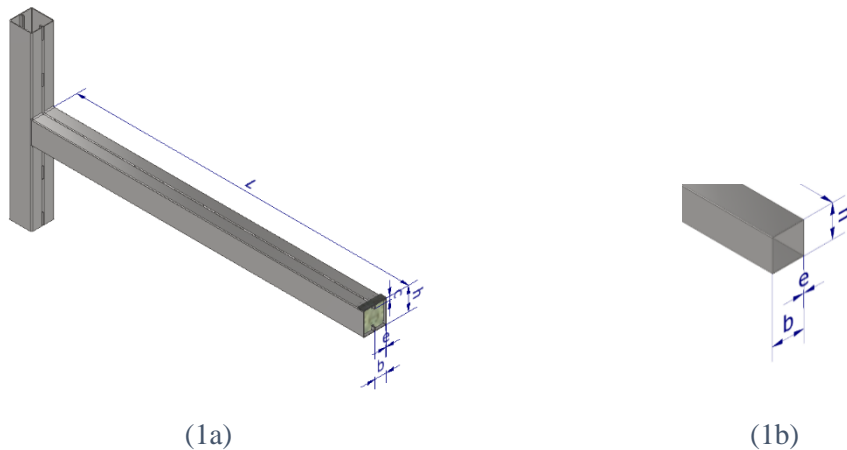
(1a) Caja con labios, unión con soldadura manual; (1b) caja sin labios, soldada de fábrica.
